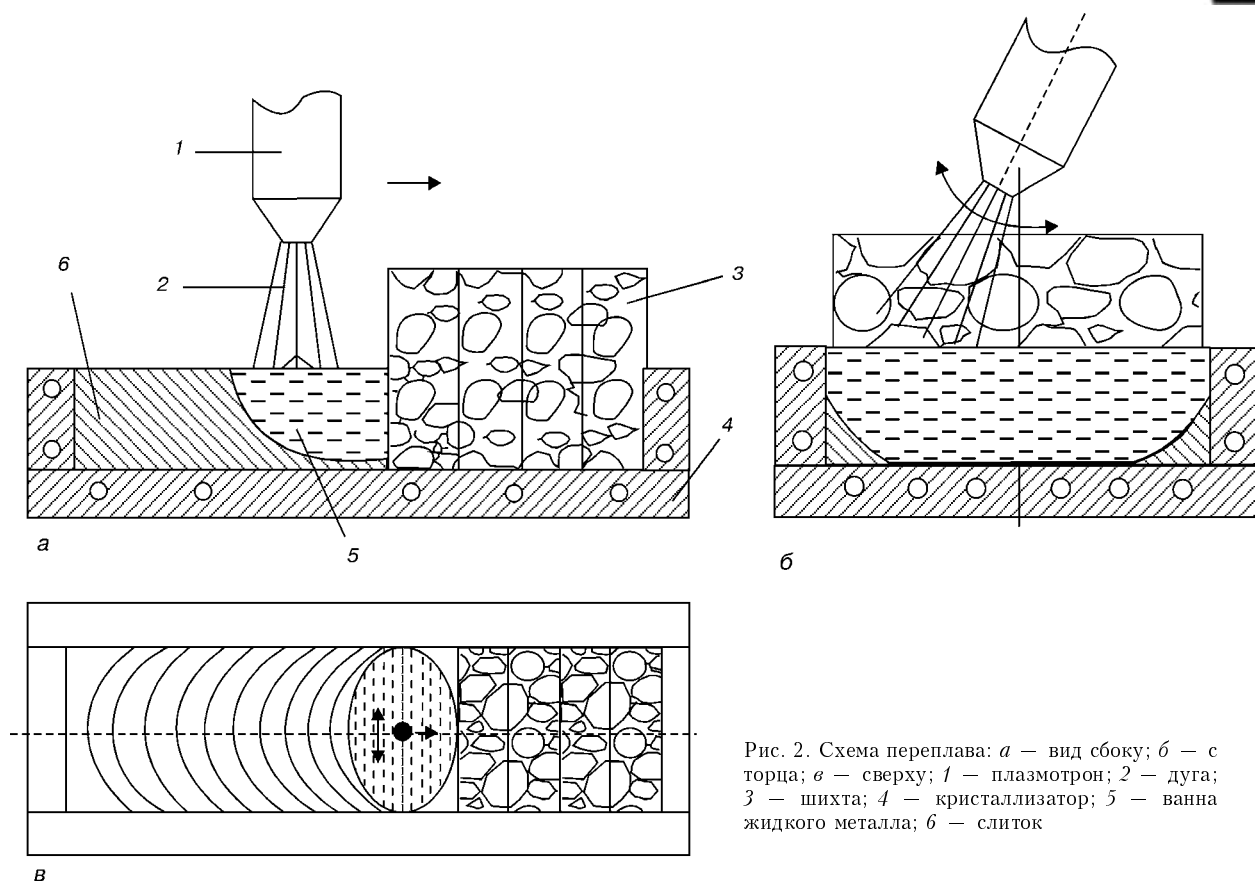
Схема переплава: *а* — вид сбоку; *б* — с торца; *в* — сверху; 1 — плазматрон; 2 — дуга; 3 — шихта; 4 — кристаллизатор; 5 — ванна жидкого металла; 6 — слиток
